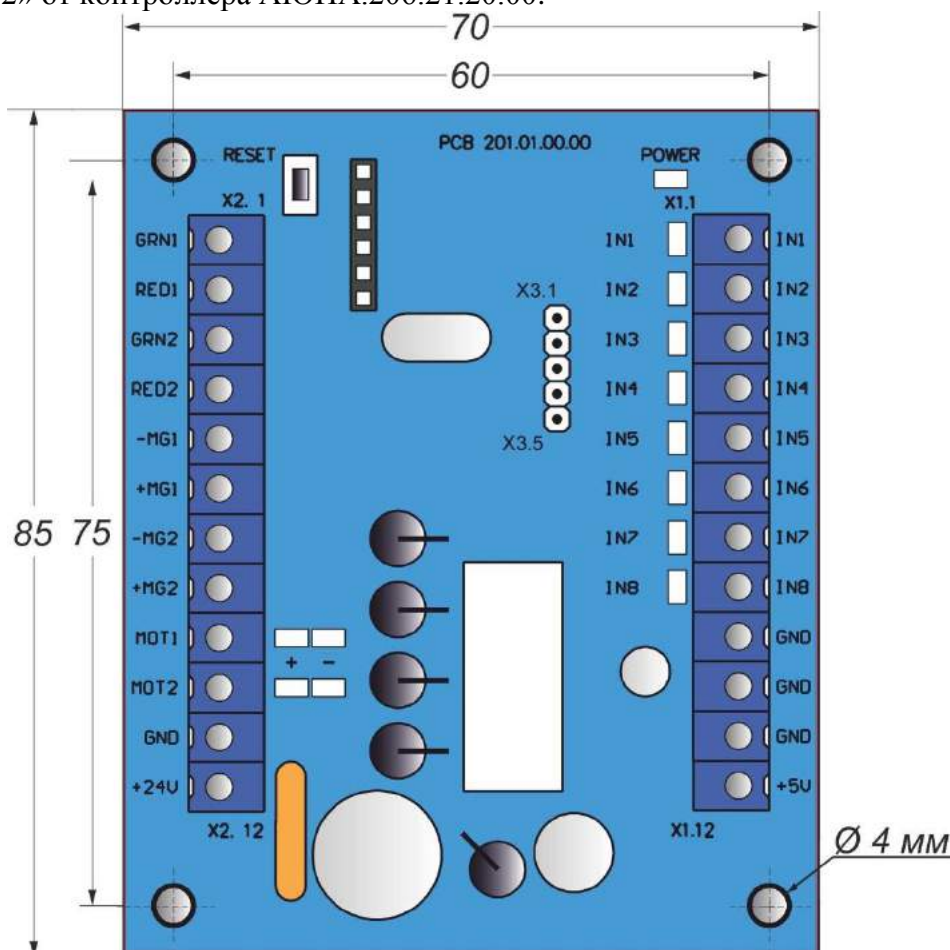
Внешний вид контроллера РСВ.201.01.00.00
